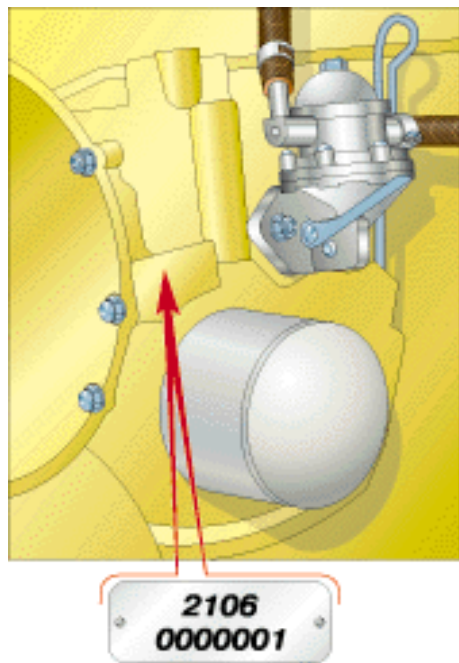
Расположение маркировки паспортных данных на блоке цилиндров двигателя ВАЗ–2106
